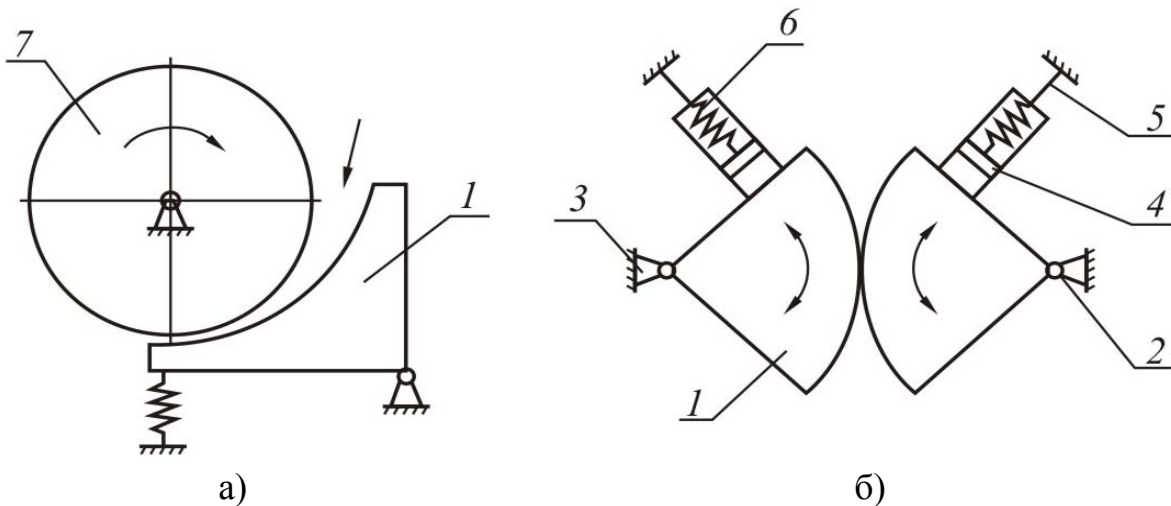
Шокові подрібнювачі: 1 - щоки; 2 - нерухомі опори; 3 - станина; 4 - пневматичні подушки; 5 - повітропровід; 6 - пружні елементи; 7 - барабан
